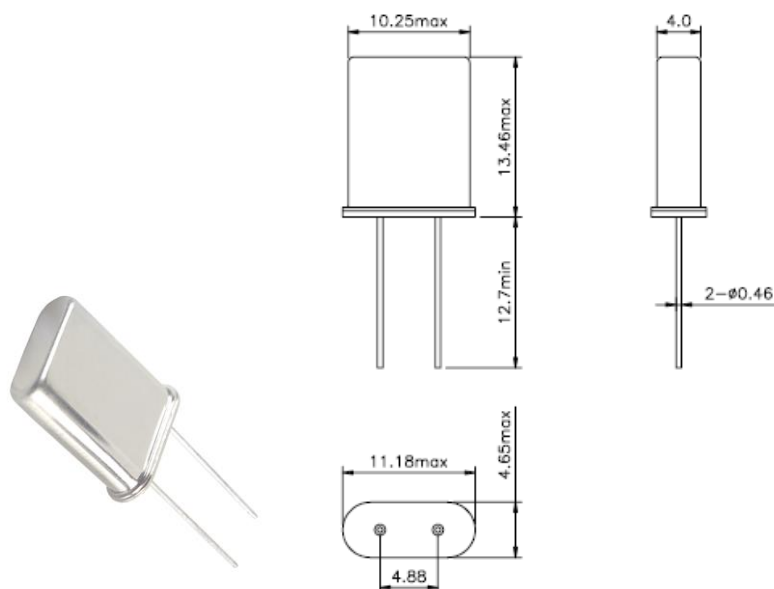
Зовнішній вигляд і габаритні розміри кварцового резонатора НС-49/U «Jauch»
